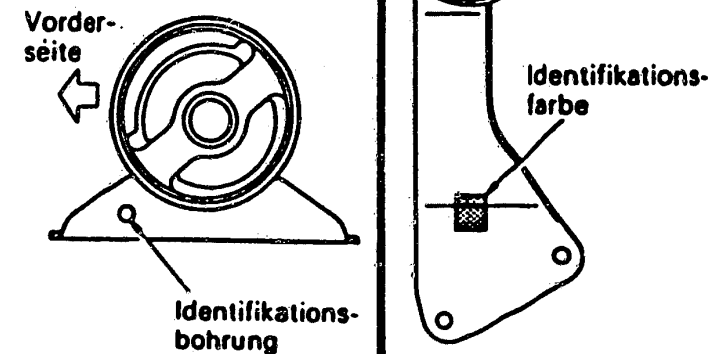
Beim Einbau der Motorlagerungen ist auf korrekte Einbaulage der Drehmomentstützen zu achten. Für den Benzinmotor mit mechanischem Getriebe ist an der bezeichneten Stelle der hinteren Stütze keine Farbmarkierung angebracht (Bild rechts).
